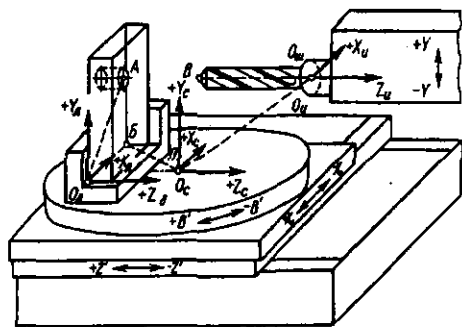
Связь систем координат детали, инструмента и сверлильно-фрезерно-расточного станка с ЧПУ
